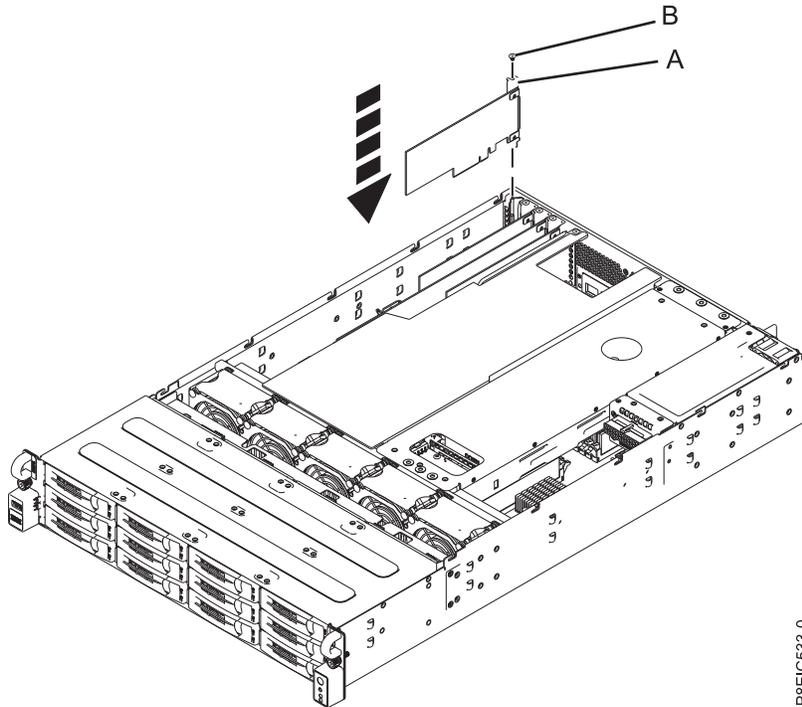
PCIe-Adapter installieren (A) und Schraube (B)
